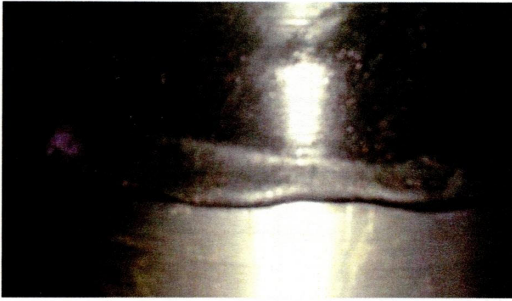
Загальний вигляд опорної частини манжети після вилучення пакера із лабораторного стенду
